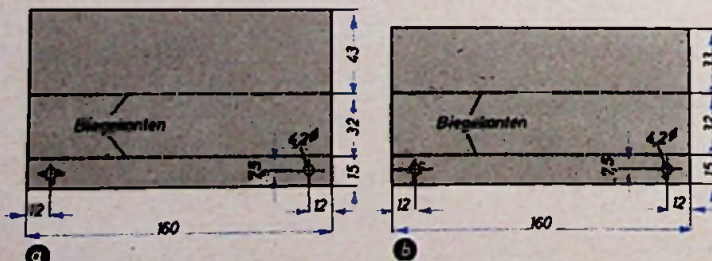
und b. Winkelstücke für die Abdeckhaube des Kopfträgers
